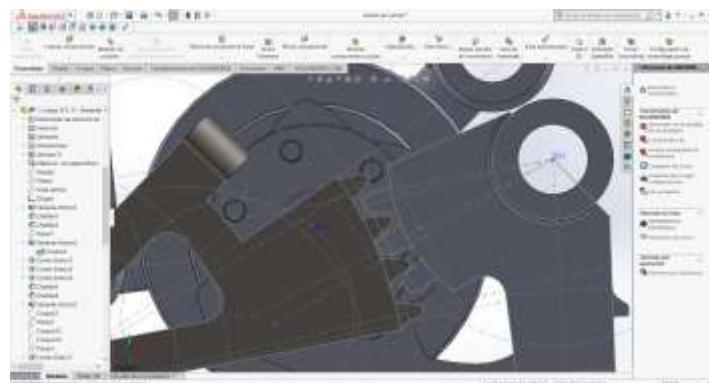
Engrane correcto entre las piezas 3Y1 y la cabeza del eje de inversión
